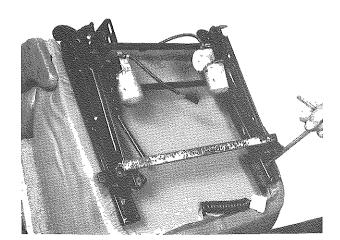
Viti di fissaggio slitte al sedile Screw fixing slides to the seat
